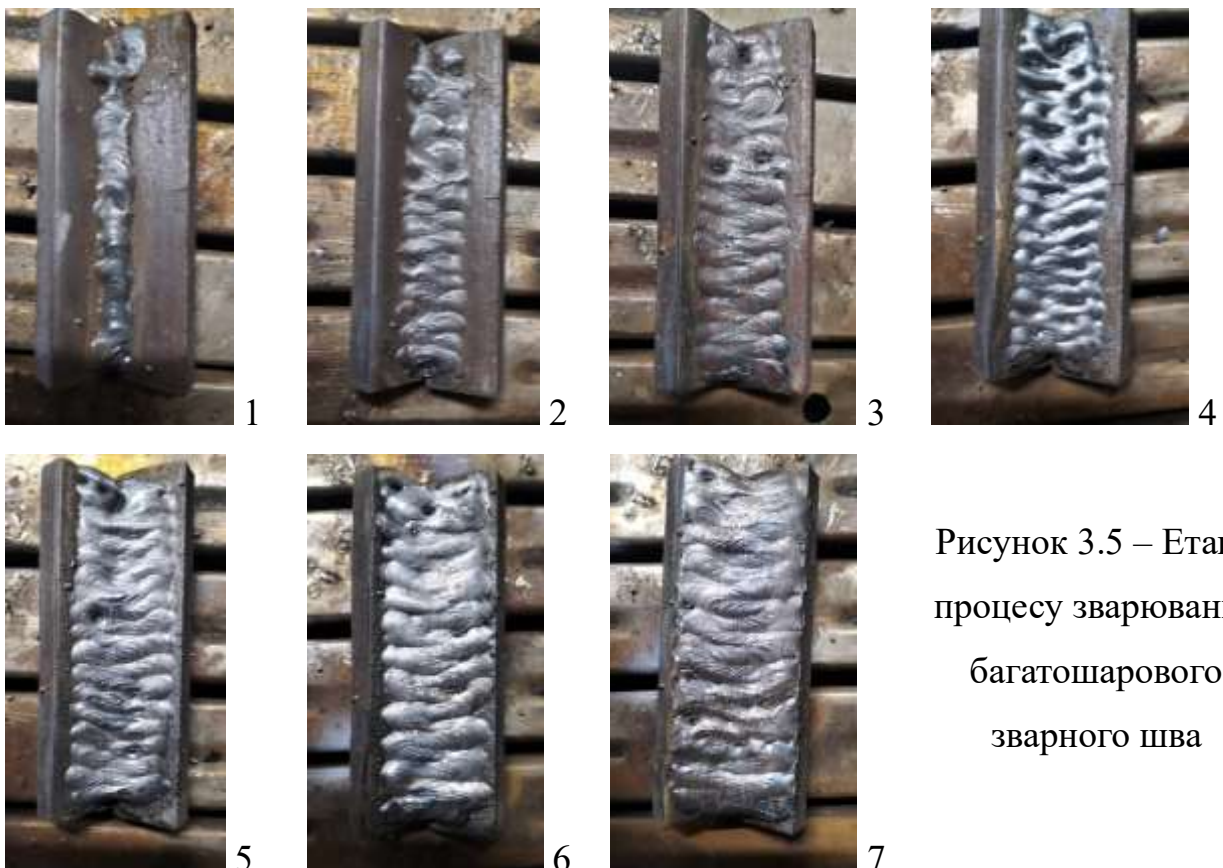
Етапи процесу зварювання багат шарового зварного шва
